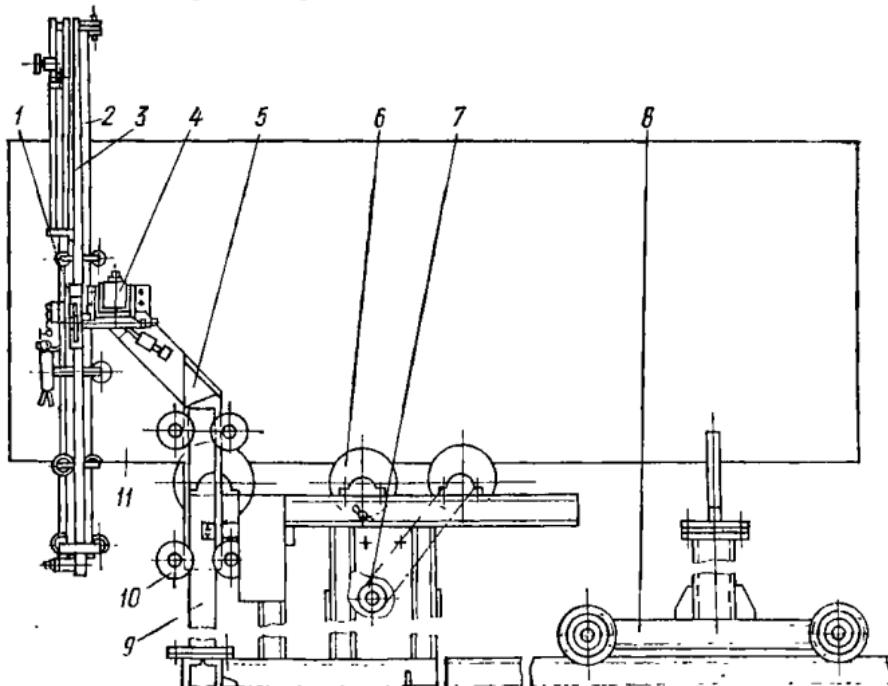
Установка УРТ-1420 для газопламенной резки труб:
